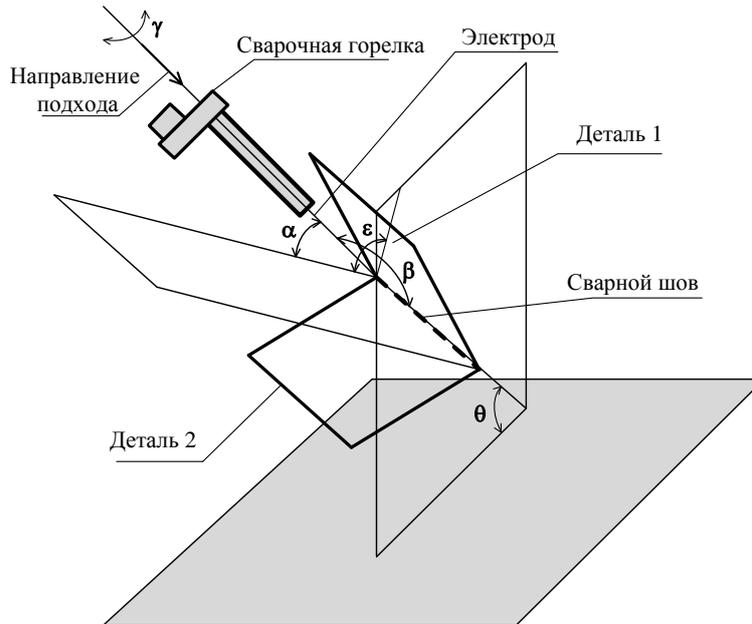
Ориентация горелки дуговой сварки и сварного шва
